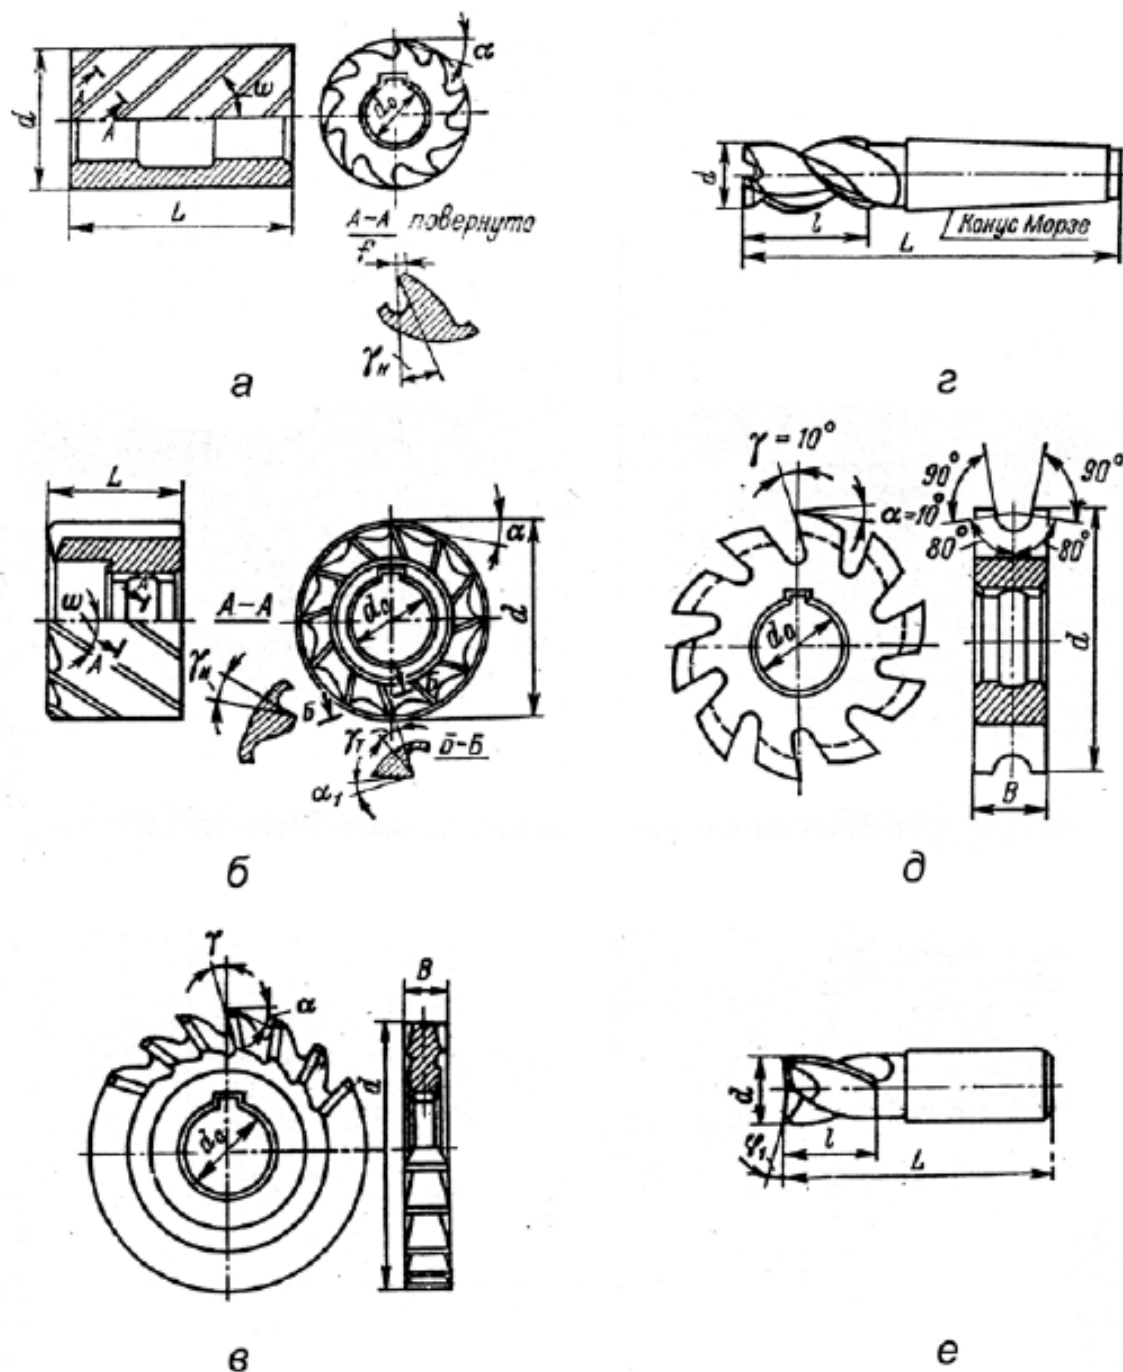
Некоторые виды конструкций фрез: а – цилиндрическая; б – торцовая; в – дисковая; г – концевая; д – фасонная; е – шпоночная
